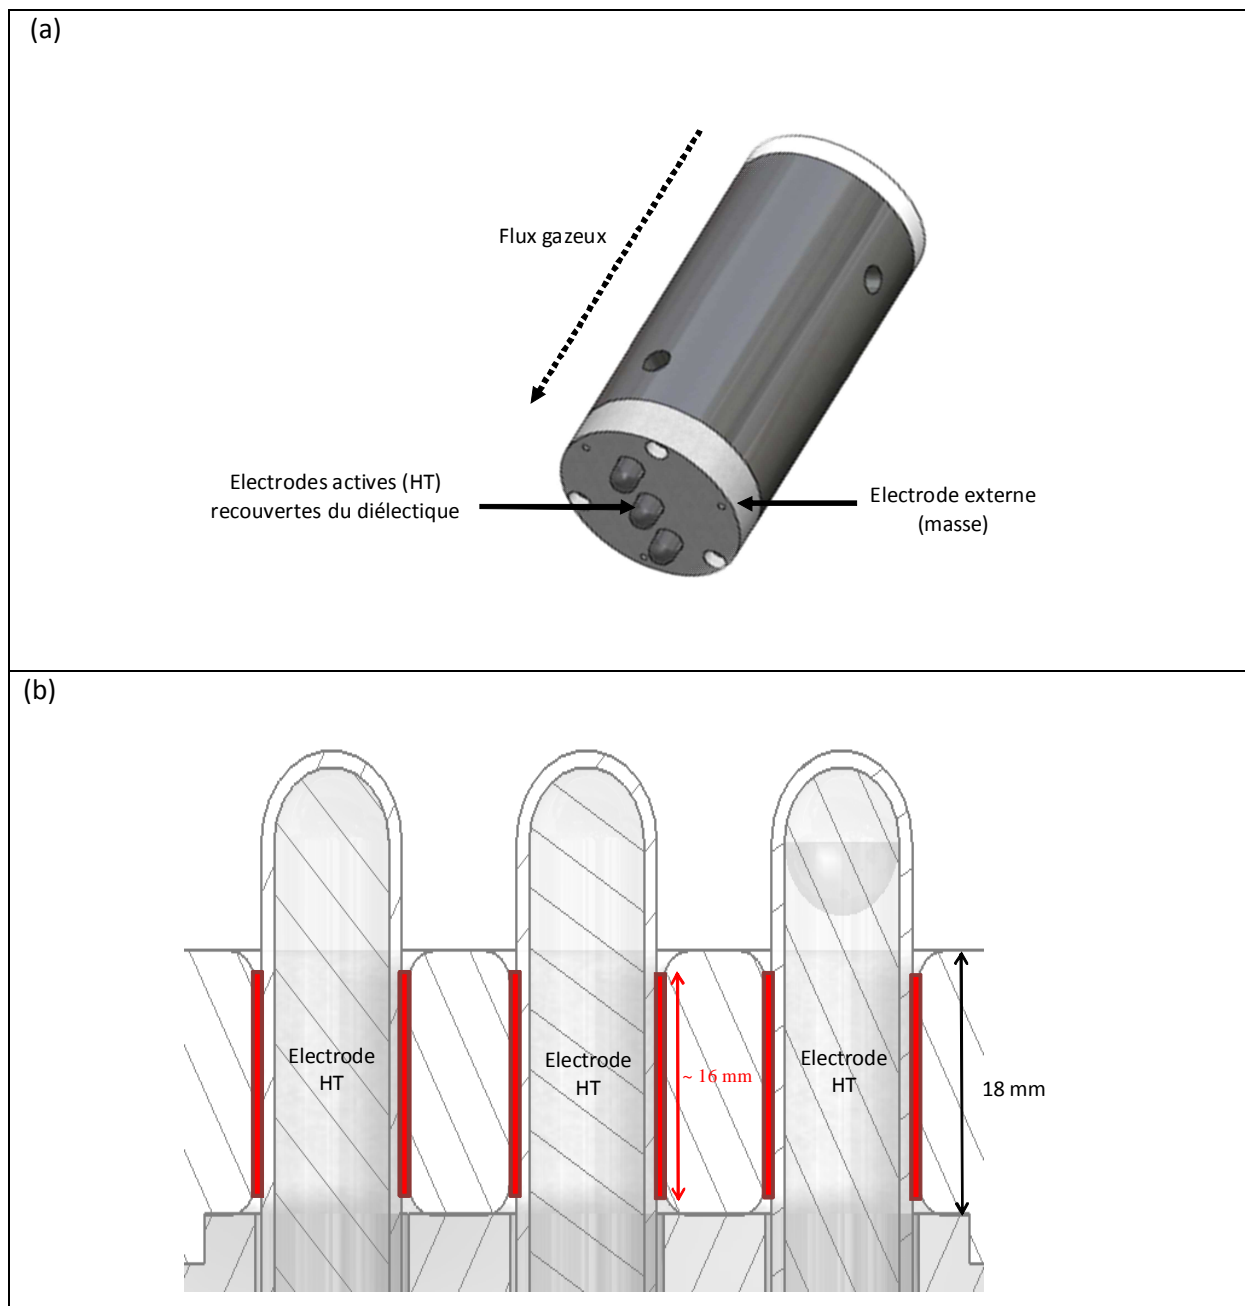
schémas du réacteur LEGP-3 têtes : (a) vue d'ensemble, (b) coupe de la zone de décharge<sup>5</sup>
